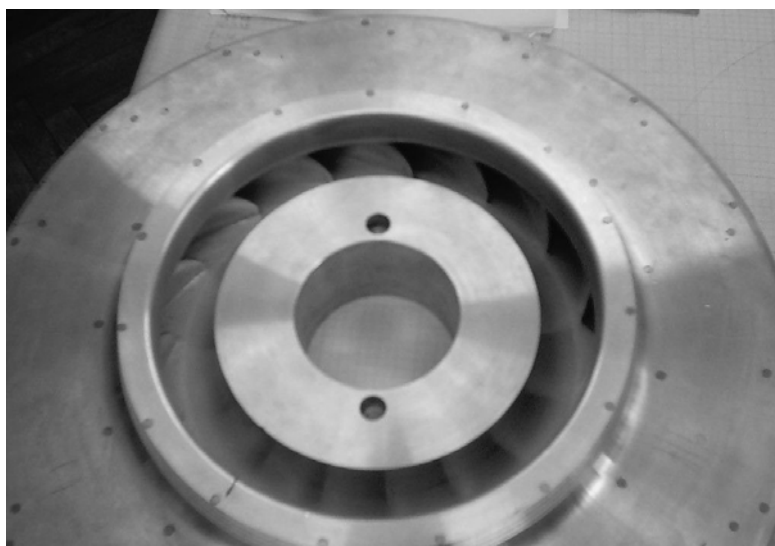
Закрытое РК с цельнофрезерованными лопатками и приклепанным покрывающим диском (кафедра КВХТ СПбГПУ)
